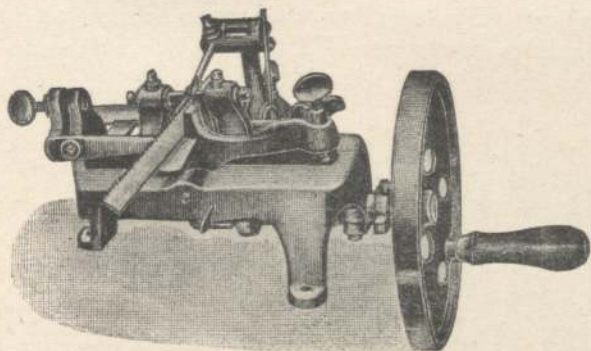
Bandsäge-Schränkmachine<sup>1</sup>. Bei dieser Maschine wird das Sägeblatt beim Schränken fest eingeklemmt. Das Blatt wird erst wieder lose, wenn der Transporteur das Blatt für den nächsten Zahn weiterschiebt. Krumme Sägeblatttrücken, wie solche oft bei den von Hand geschränkten Sägeblättern entstehen, gibt es bei dieser Maschine nicht mehr.
